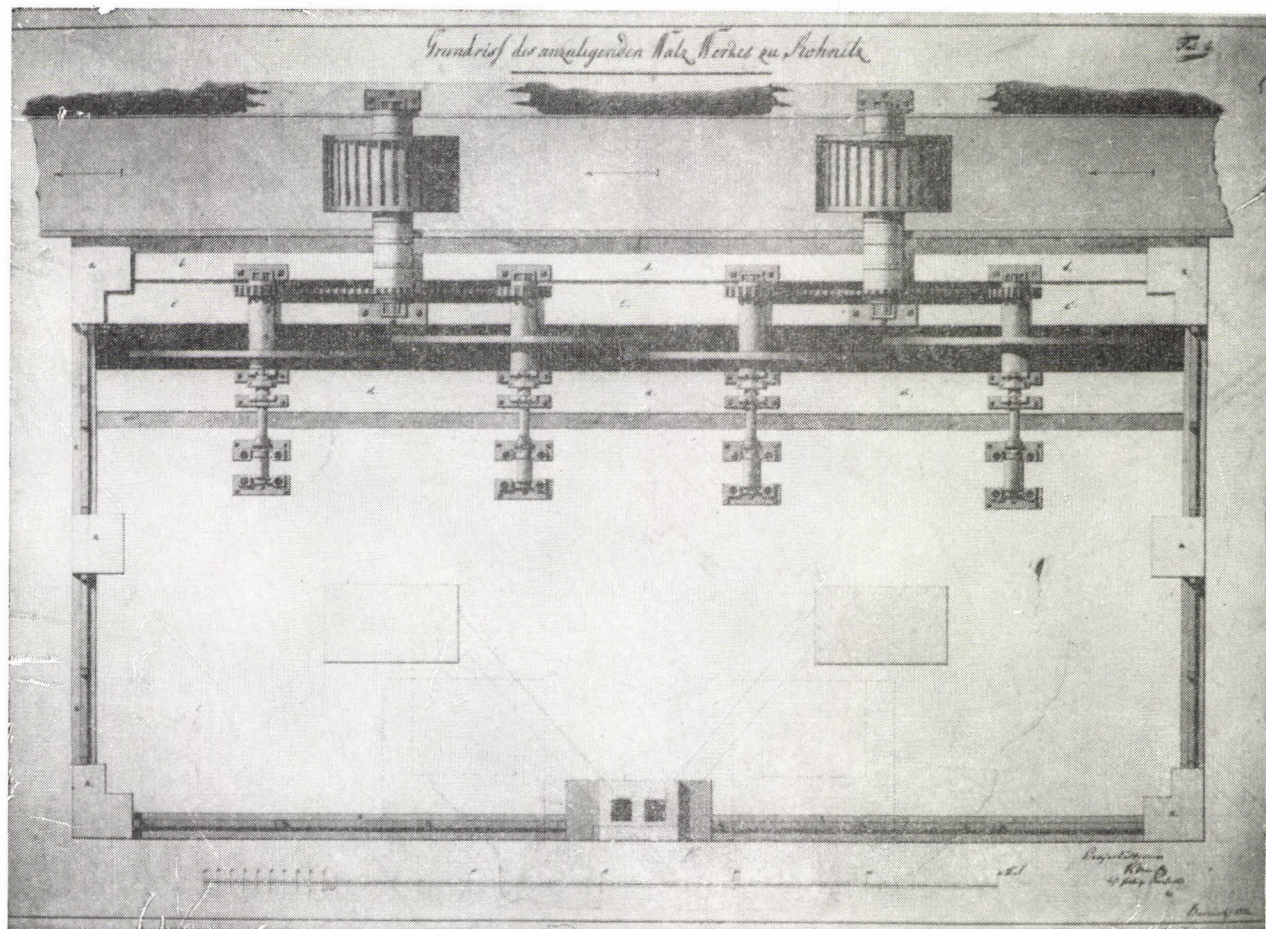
Rohnitzer Blechwalzwerk — Entwurf aus dem Jahre 1813, Grundriß
